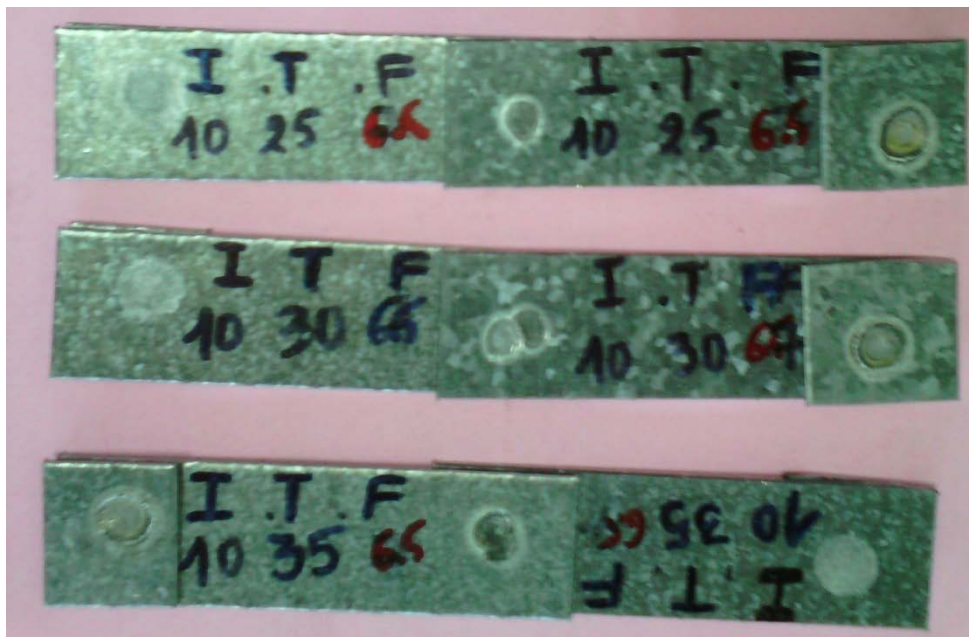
Assemblage soudé par point des éprouvettes Z275
